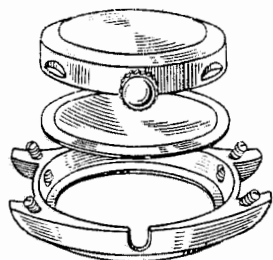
Влагозащитный корпус защелкивающегося типа.
